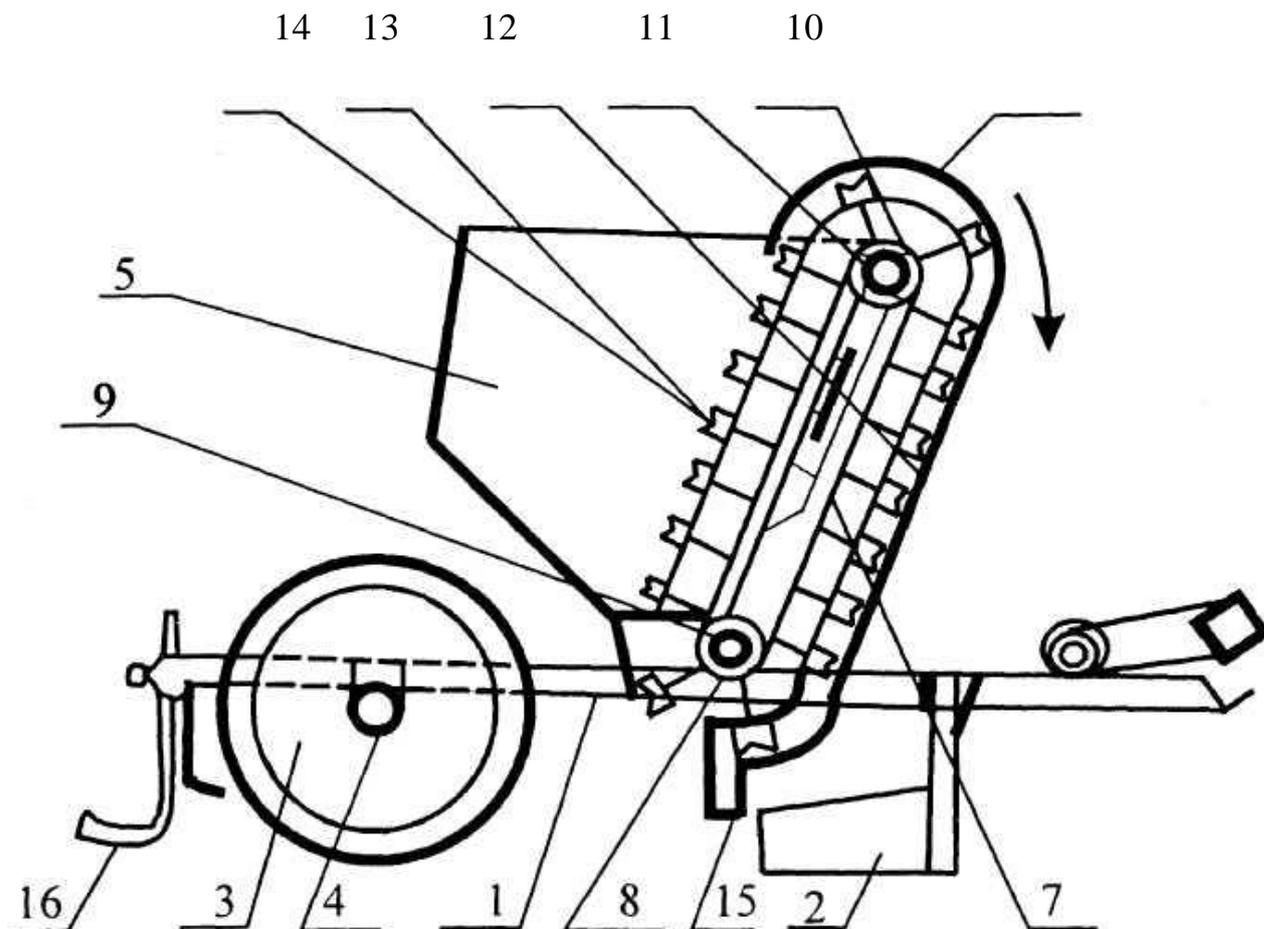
Схема цепочно-ложечного аппарата: 1 – рама; 2– сошник анкерный; 3 – колесо прикатывающее; 4 – ступица; 5 – бункер; 6 – направляющие; 7 – цепь; 8 – звездочка ведущая; 9, 11 – валы; 10 – звездочка натяжная; 12 – лапка; 13,14 – ложечки; 15 – горловина; 16 – загортач
